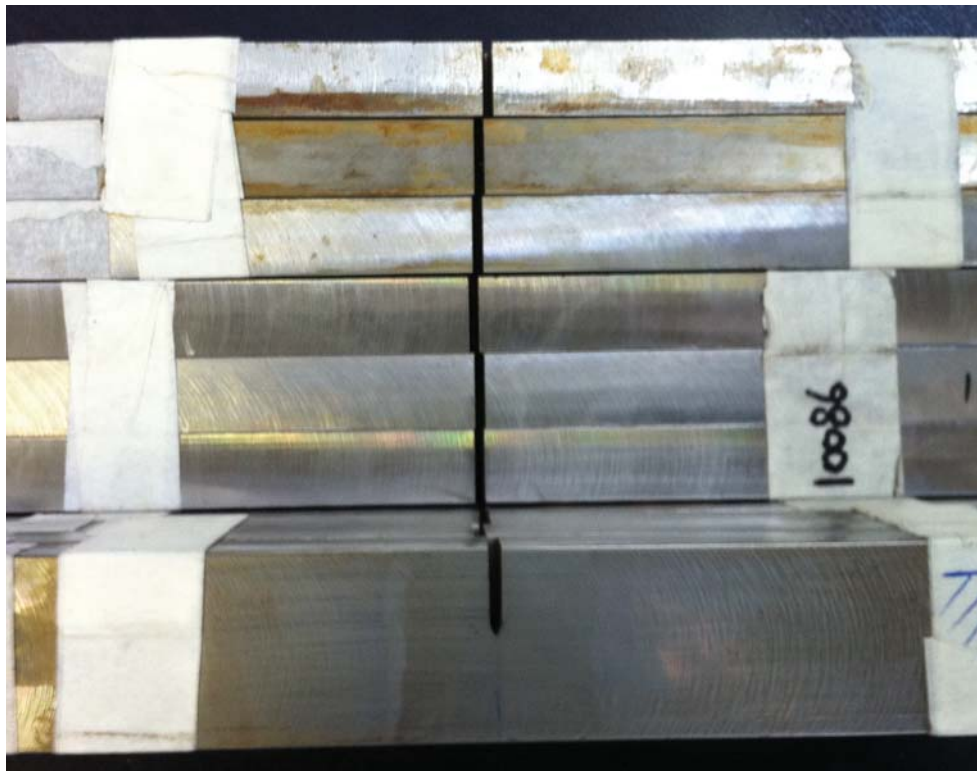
Corpos de prova SE (B) (solda) após realização do entalhe – Vista superior + Seção transversal
